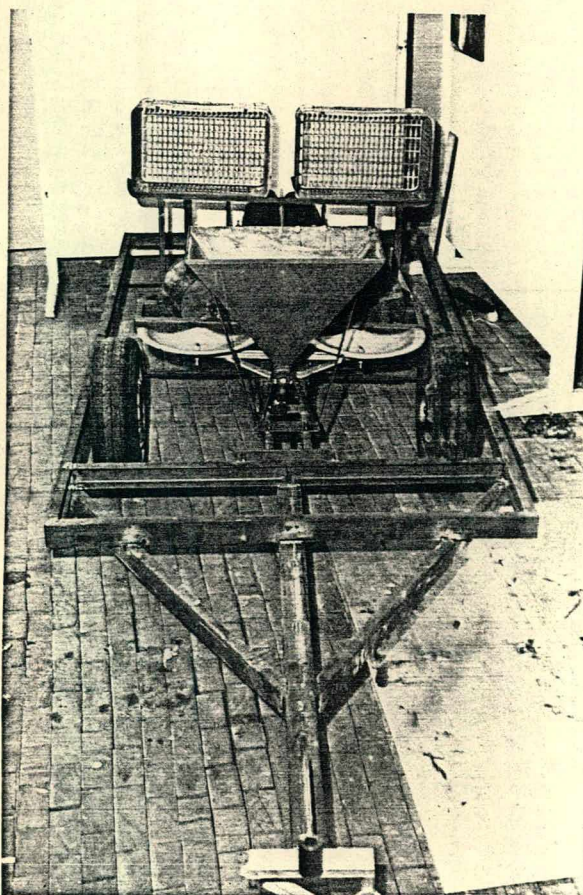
Vista de frente após a montagem final dos componentes.
